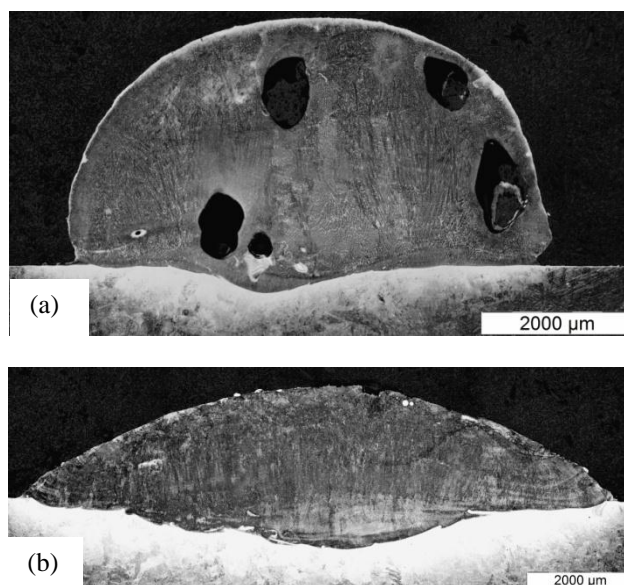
Cordão de solda de Cavitec (a) Cav17Ar, (b) Cav22Ar
